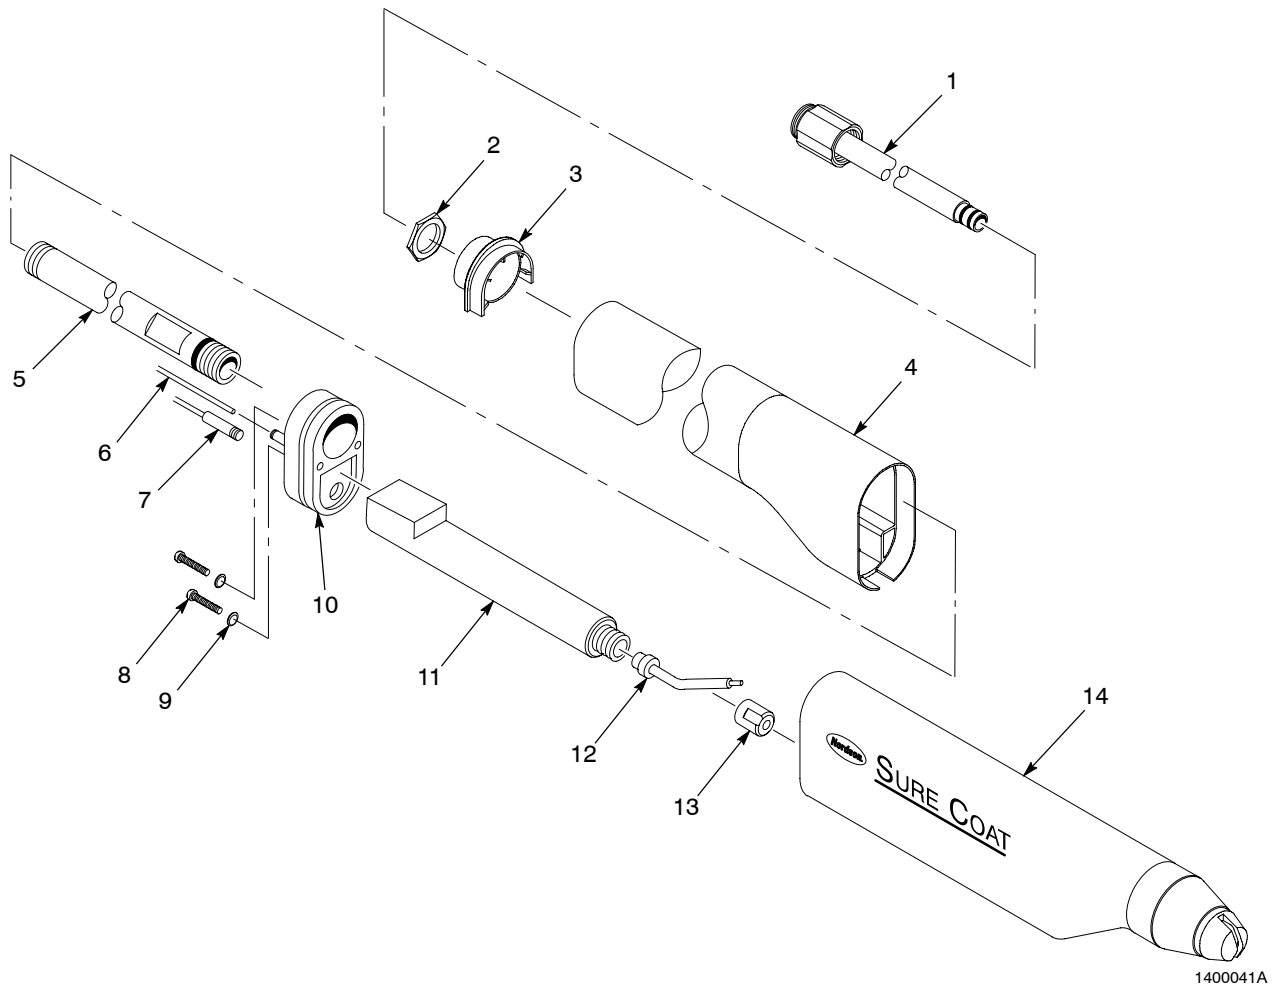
Sostituzione del moltiplicatore della pistola con montaggio su tubo
